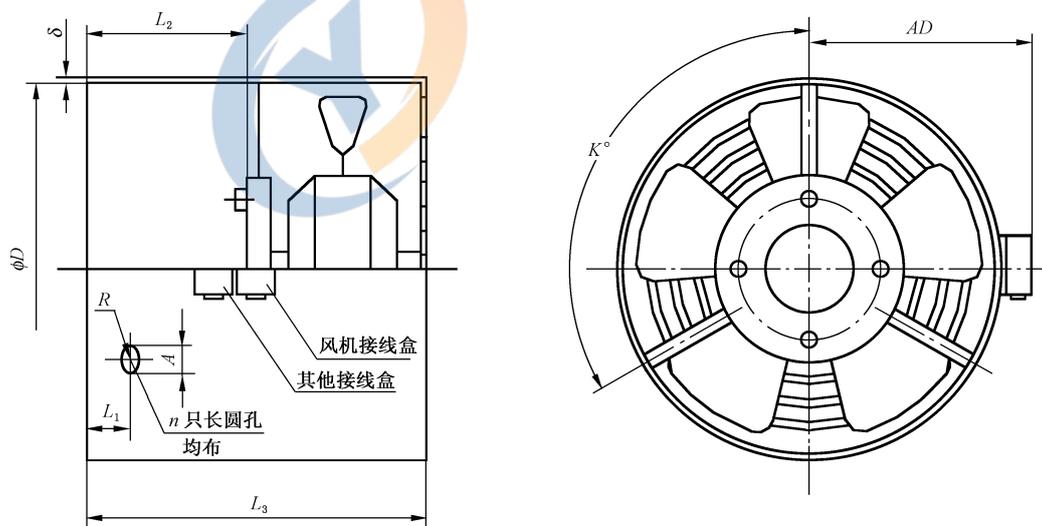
单支撑安装结构的风机安装尺寸和外形尺寸
